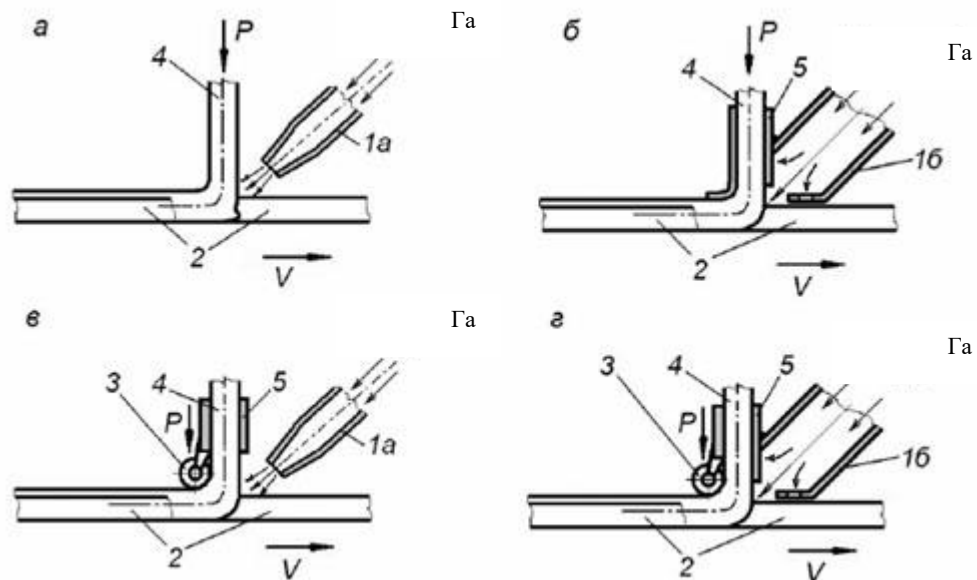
Схеми зварювання пластмас присадним прутком:
